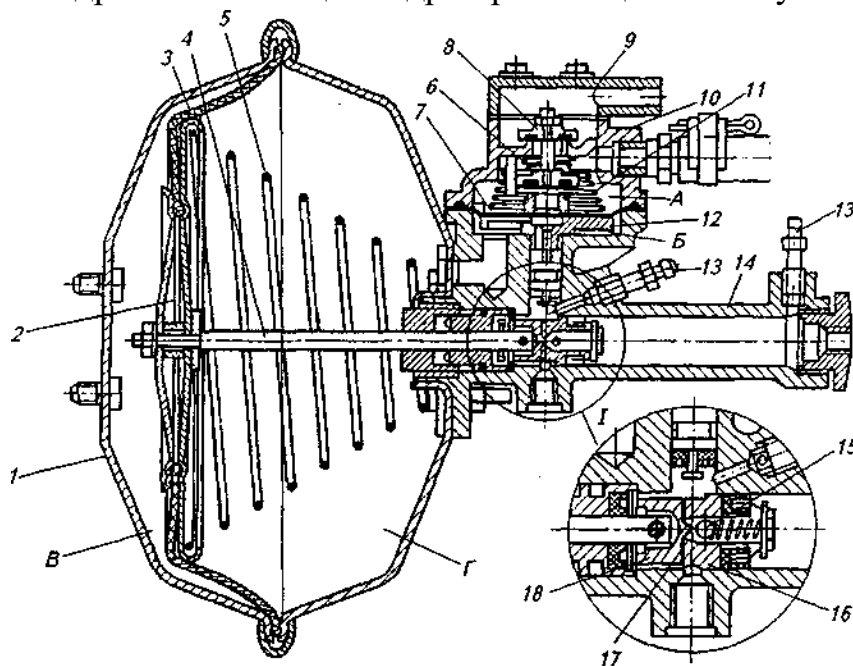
Гидровакуумный усилитель тормозов: А, Б — полости клапана управления; В, Г — полости камеры; 1 — камера усилителя; 2 — тарелка диафрагмы; 3 — диафрагма усилителя; 4 — толкатель
